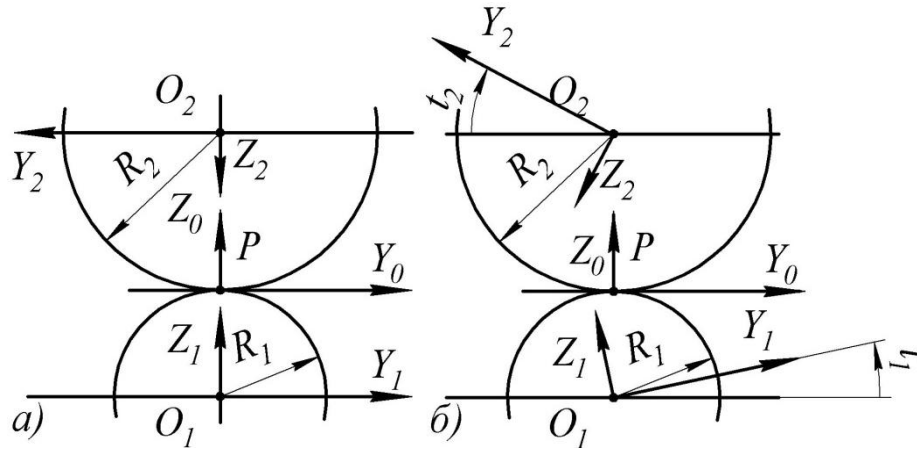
Схема формоутворення при коченні початкового кола деталі по початковому колу інструмента
